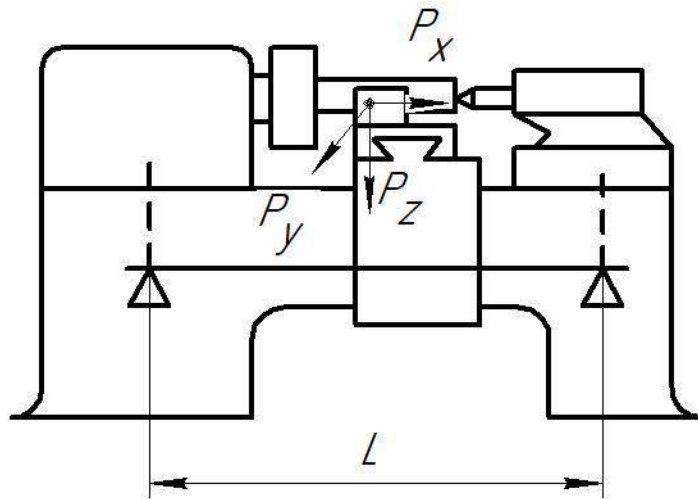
Розрахункова схема базової деталі токарного верстата
